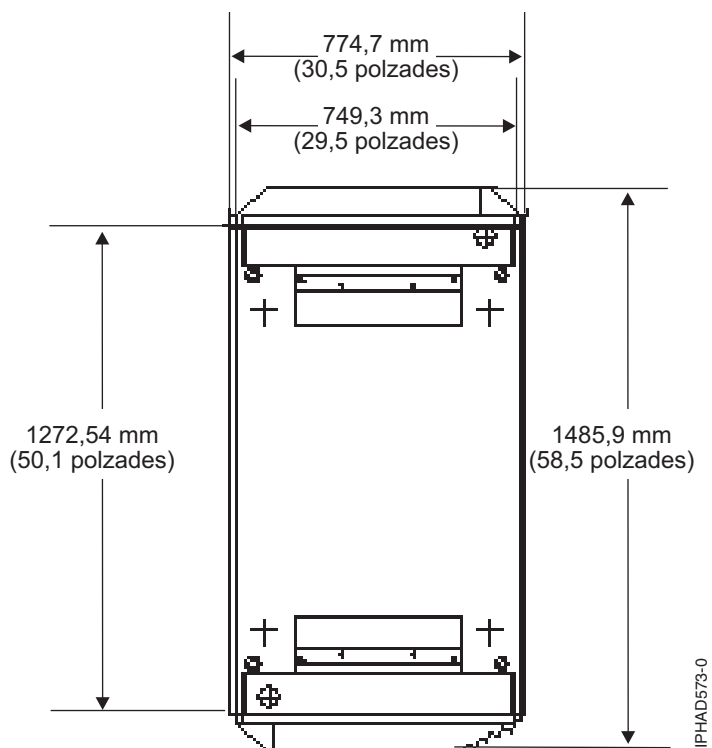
Vista de planta per a sistemes d'un sol bastidor amb portes extraplans
